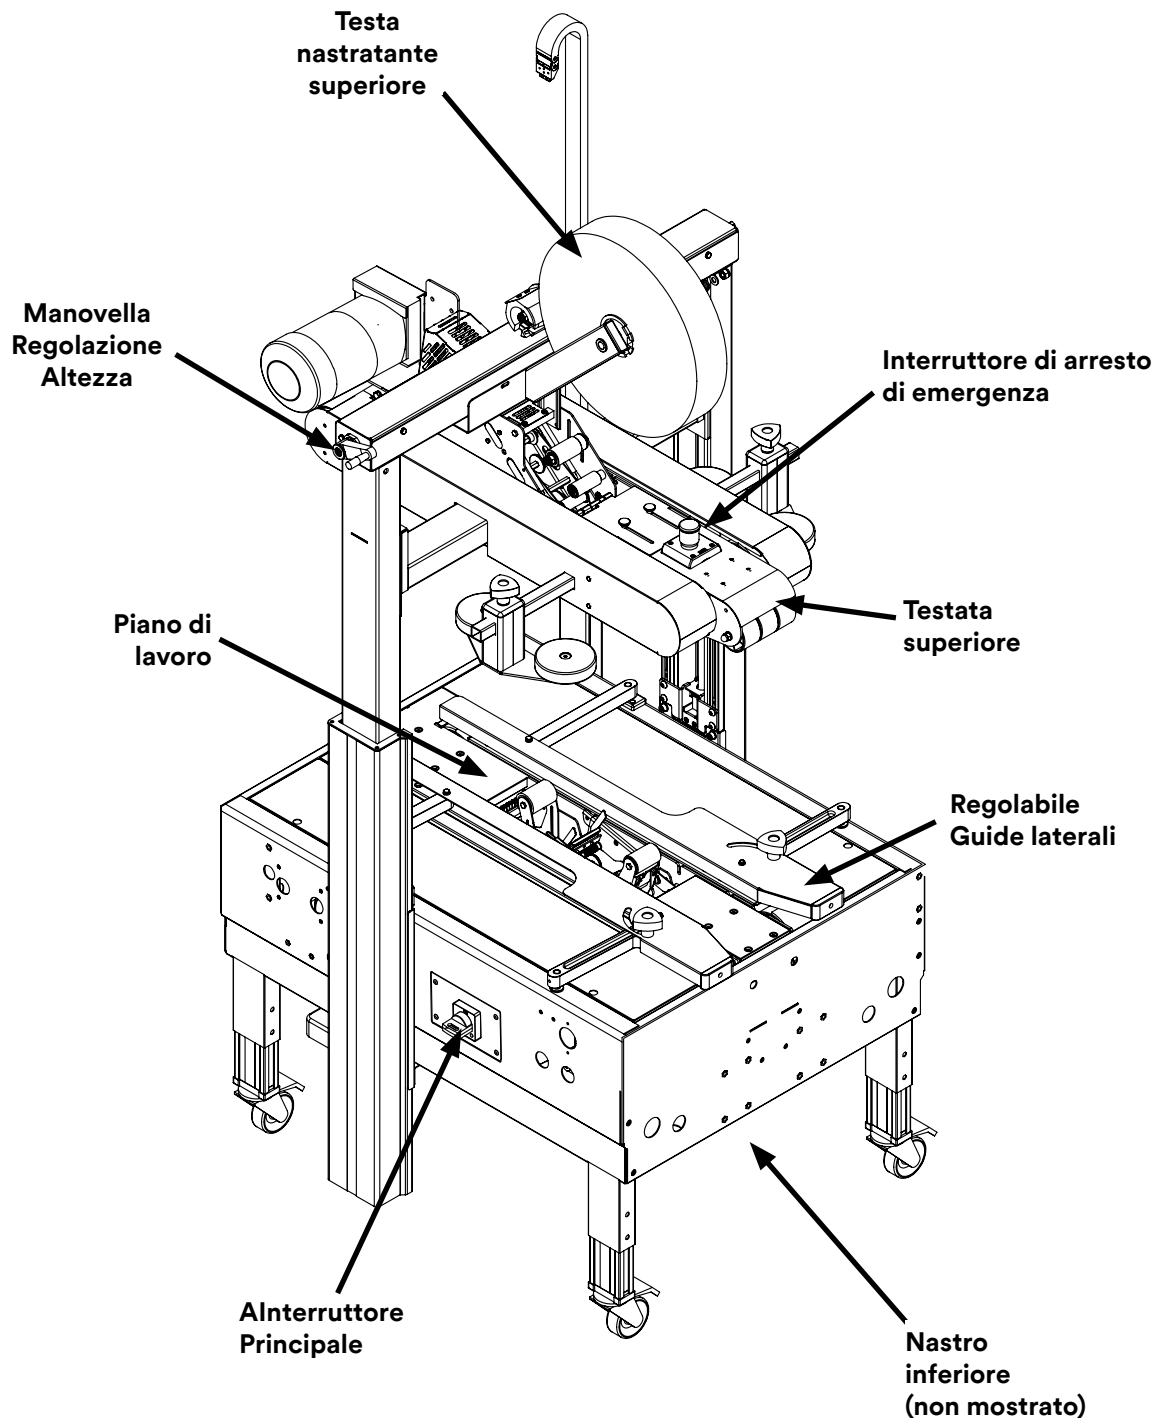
7000a-I / 7000a3-I Pro Componenti del sistema di sigillatura (Vista frontale sinistra)
